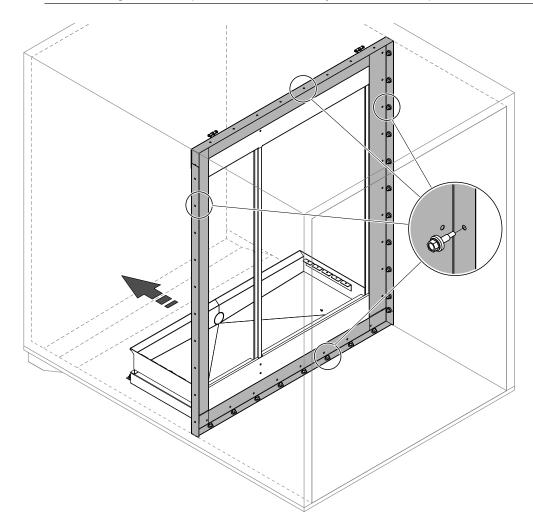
Montaje de las chapas de obturación Condair opcionales en el lado de entrada de aire
